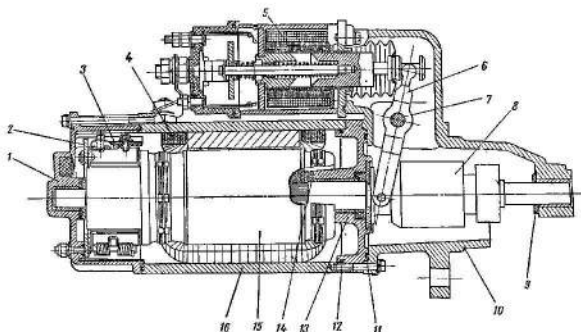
Стартер: 1 – крышка со стороны коллектора; 2 – траверса; 3 – изолированная щетка; 4 – обмотка возбуждения; 5 – электромагнит привода включения; 6 – рычаг; 7 – ось рычага; 8 – привод стартера; 9 – упорная шайба; 10 – крышка со стороны привода; 11, 12 – уплотнительные кольца; 13 – промежуточный подшипник; 14 – упорная шайба; 15 – якорь; 16 – корпус.
